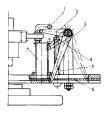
杠杆传动闸门式送料机构 1—压头; 2—摆杆; 3—推杆; 4—顶杆; 5—弹簧; 6—推板; 7—料匣
